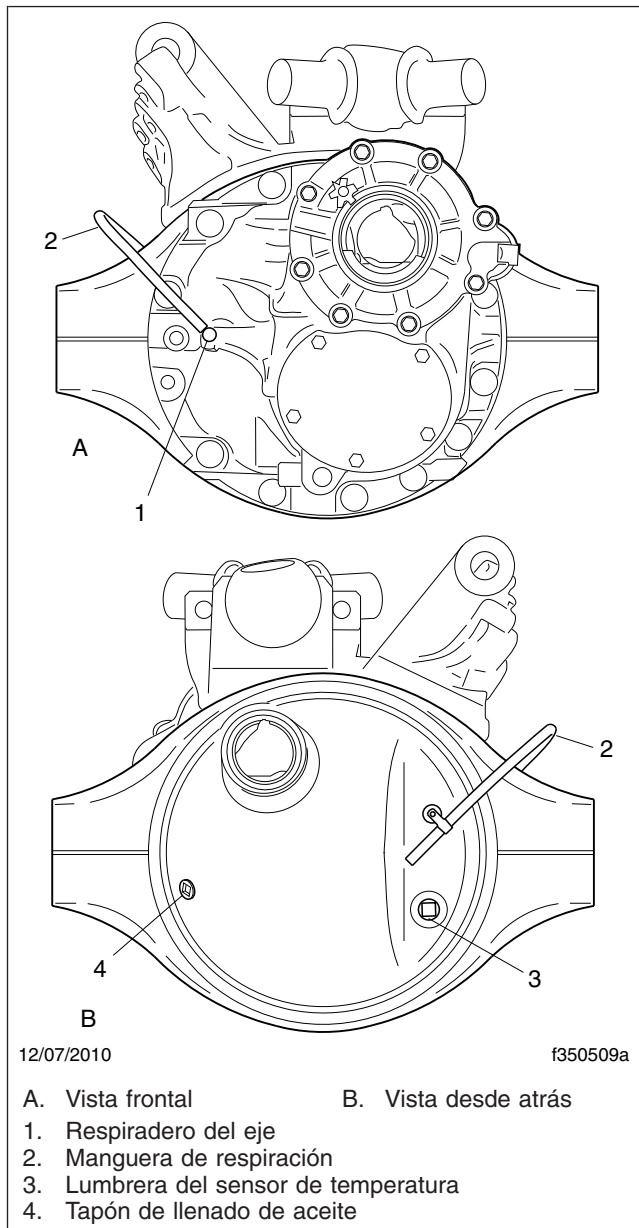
, Eje en tándem Detroit (se muestra el eje anterior)
